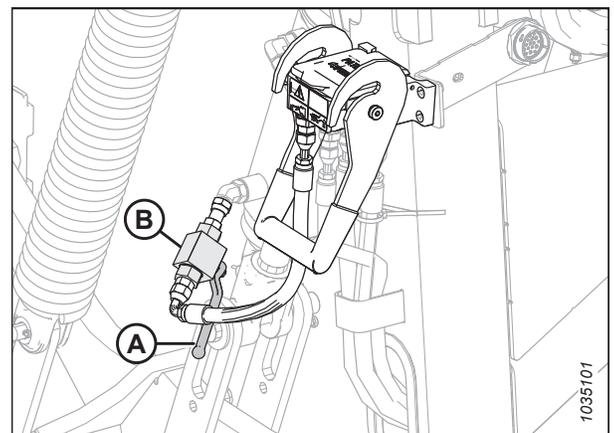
Verriegelungsventil des Hubzylinders für TM100 – linke Seite
